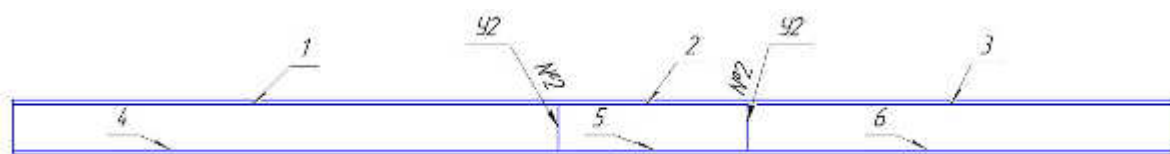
Порядок выполнения сварных швов
